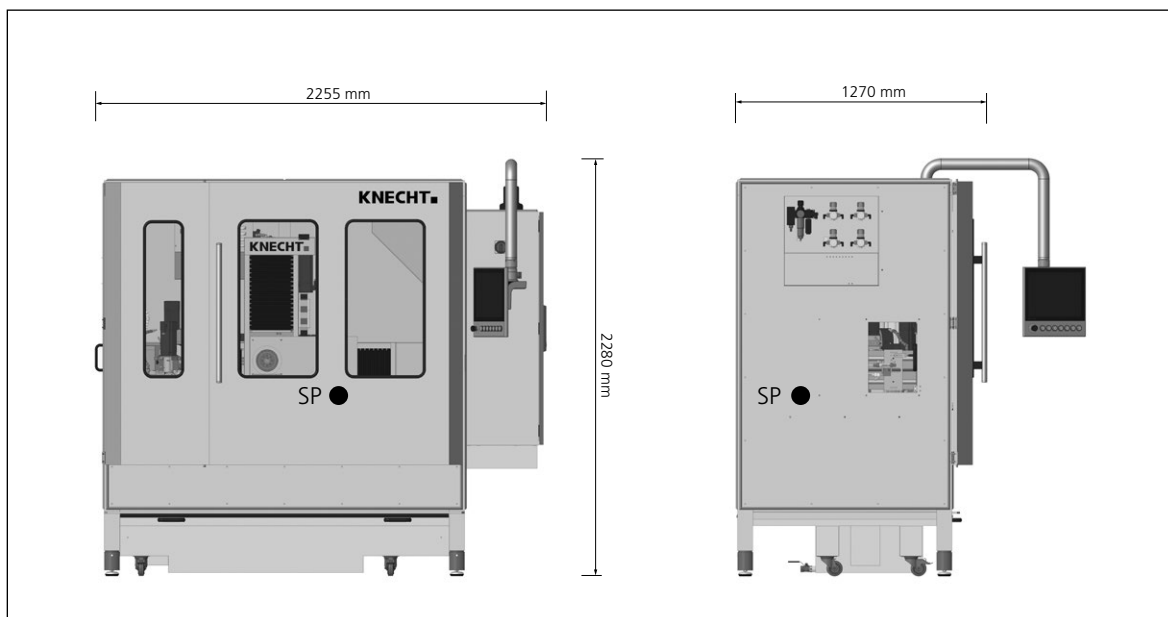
Dimensions en mm et centres de gravité (SP) de la machine
